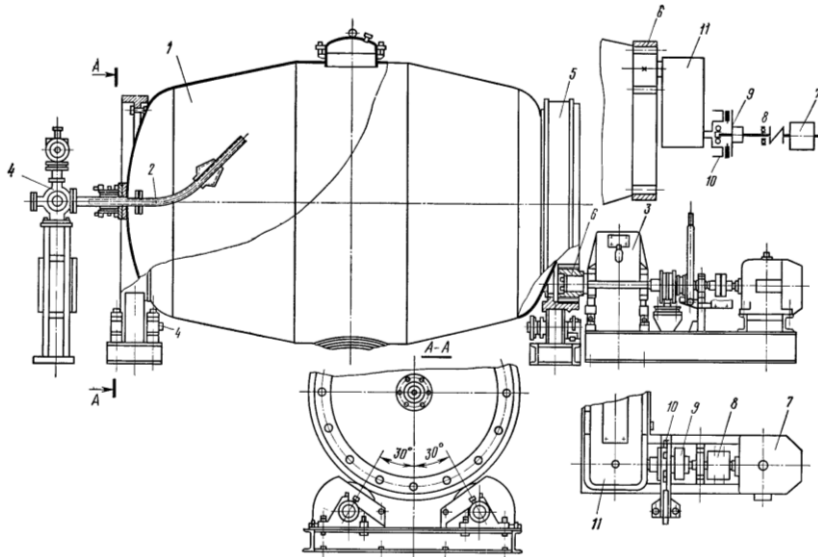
Гасильний барабан: а – загальний вигляд агрегату та кінематична схема приводу обертання корпусу, б – схема пароводопідвідного пристрою:
